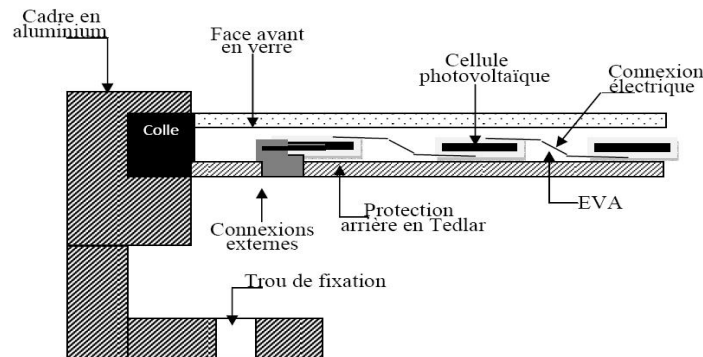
Vue en coupe d'un module photovoltaïque [11]
